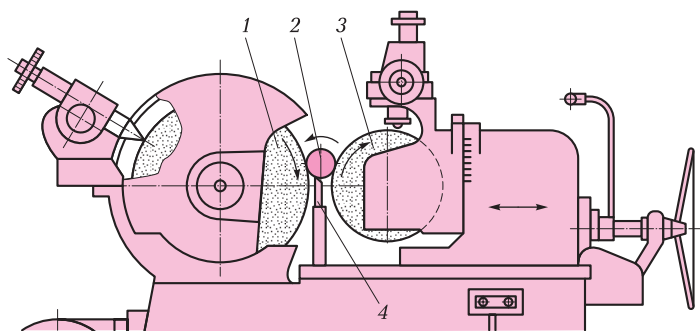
Общий вид бесцентрово-шлифовального станка
